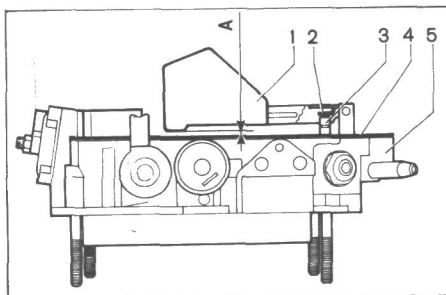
Установка уровня топлива в карбюраторе: 1 — поплавок; 2 — язычок; 3 — игольчатый клапан; 4 — прокладка; 5 — крышка карбюратора
